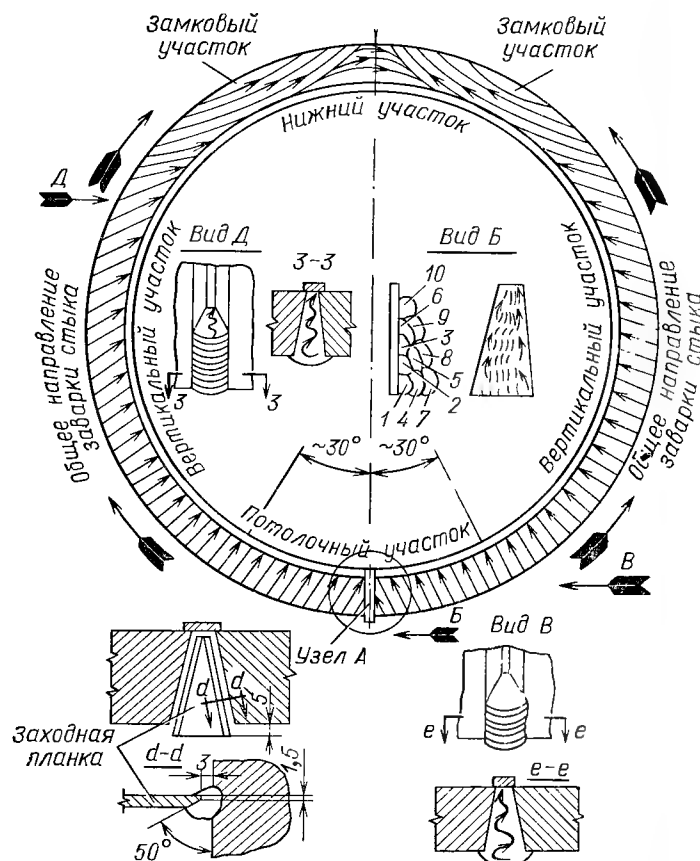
Схема сварки способом «поперечной горки» неповоротного вертикального стыка.
